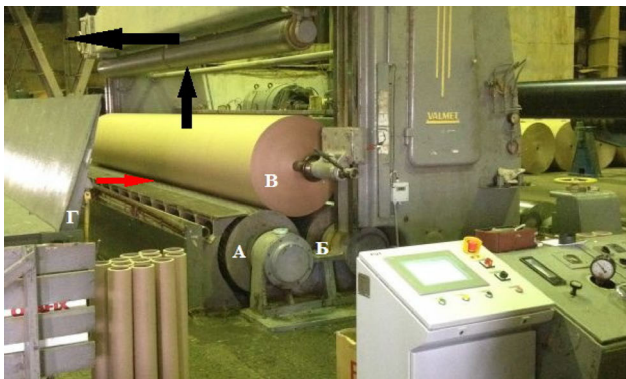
Бобинорезательная машина: А, Б – металлические валы цилиндрической формы; В – тамбурный вал с рулоном бумаги; Г – металлическая платформа для операторов (поднята); черные стрелки – направление движения рулона бумаги, красная стрелка – направление затягивания тела пострадавшего в станок
